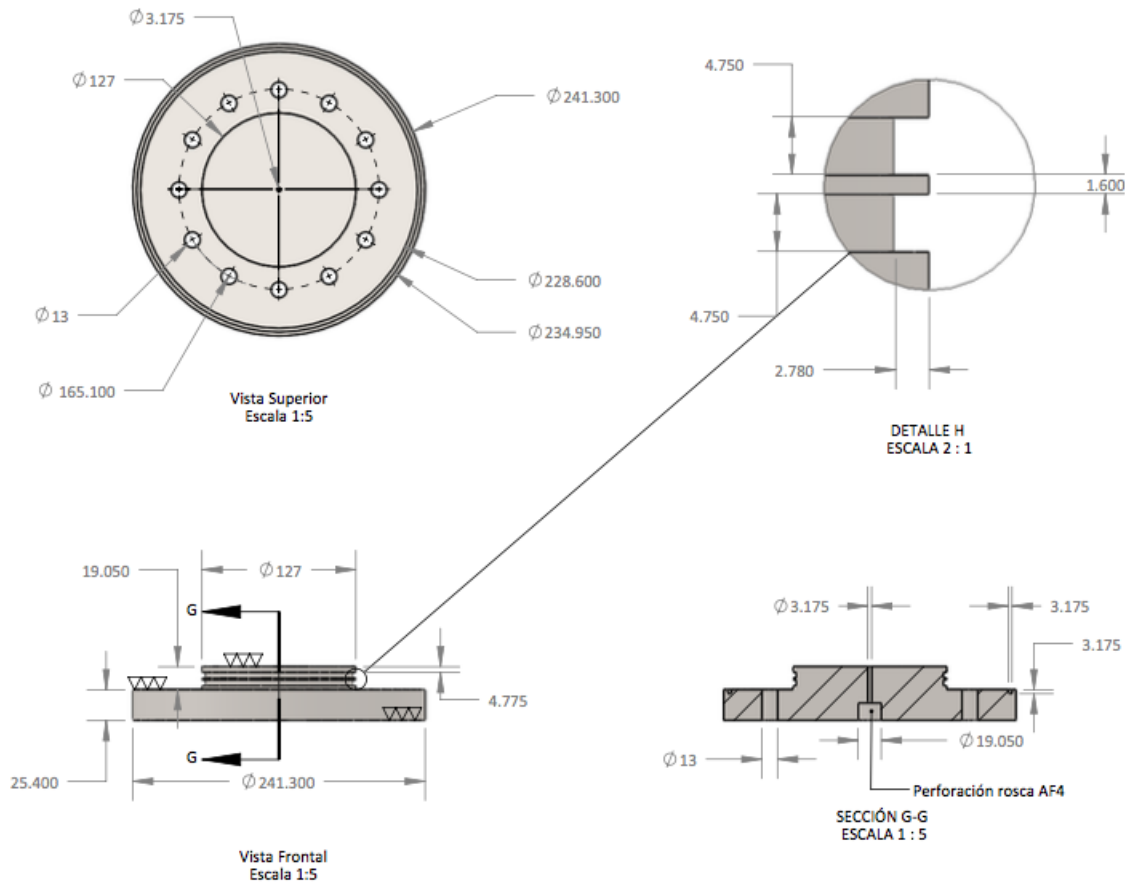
Detalles del elemento de cierre del reservorio. La vista superior muestra la distribución orificios para los 12 tornillos que ajustan la cubierta al cuerpo cilíndrico. Además de la dimensiones de la cubierta la vista frontal indica que el acabado de cada superficie es de tipo pulido. El detalle H presenta las dimensiones de los dos canales para los O-rings que forman el sello entre la cubierta y el cuerpo cilíndrico. La sección G-G indica que la conexión a la línea de dióxido de carbono es estándar del tipo AF4 de *High Pressure Equipment Company* para presiones de servicio de hasta 68.94 MPa. Las dimensiones de las cotas presentadas son milímetros.
